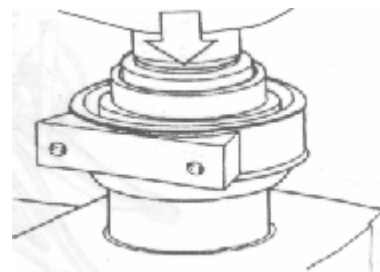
Установка подшипника в сепаратор. Вверху и внизу показан применяемый инструмент
